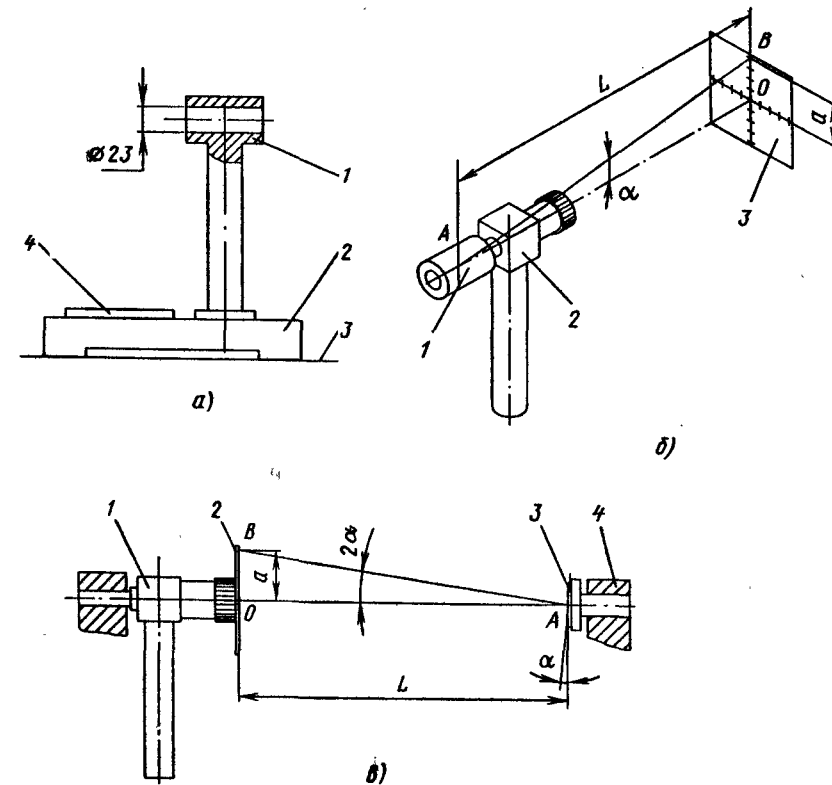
Измерения с помощью лазерного излучателя ИЛХП-23: а – технологическое приспособление: 1 – держатель; 2 – корпус; 3 – привалочная поверхность; 4 – площадка под квадрант; б – схема измерений методом визирования: 1 – контролируемый объект; 2 – лазерный излучатель; 3 – мишень; в – схема измерений методом авторефлексии: 1 – лазерный излучатель; 2 – мишень; 3 – зеркальный датчик; 4 – контролируемый объект
